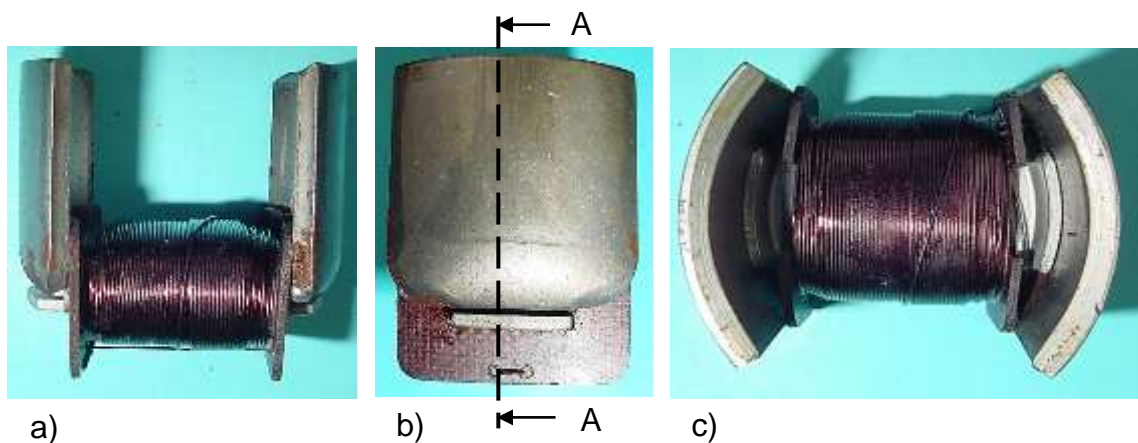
Anker: a) Seitenansicht des Ankers, b) Pol mit unterem Jochblech, c) Ankerspule und Stirnseiten der Pole
